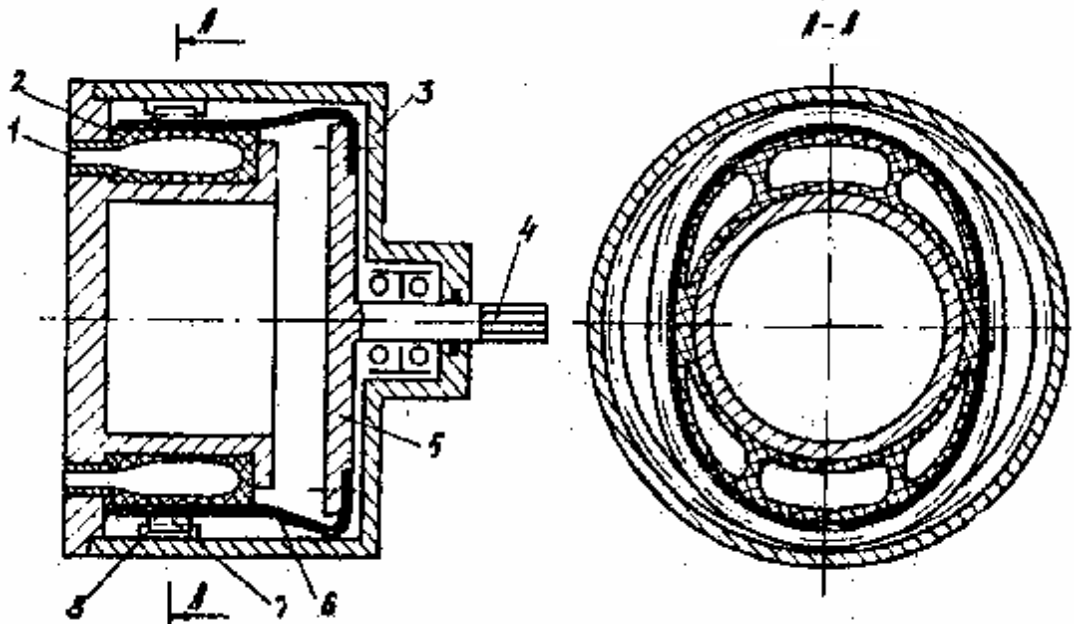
Трехтактный эластично-камерный шаговый гидромотор с волновой передачей
